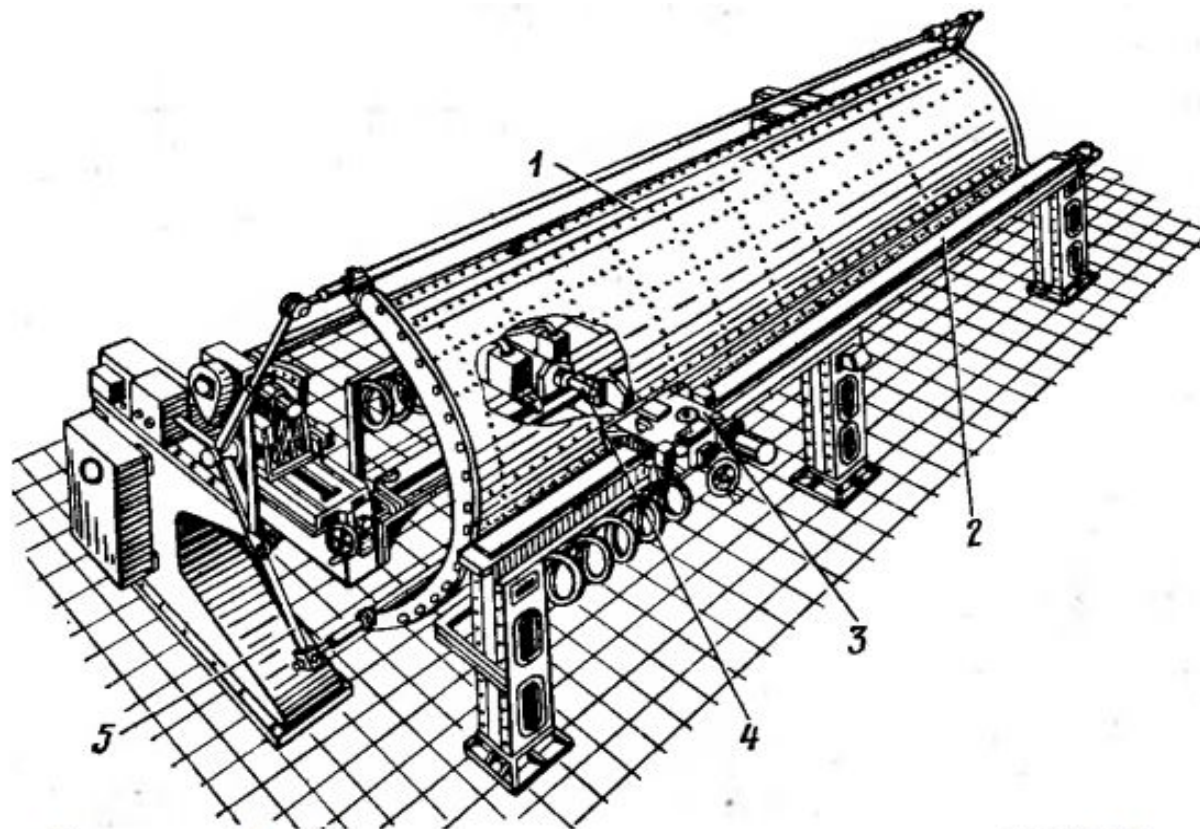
Сверлильно-зенковальная установка СЗУ-Ф1:
